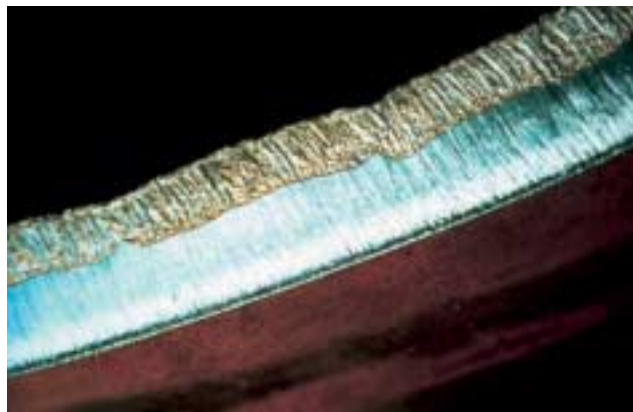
Schnitt durch eine Verschleißverbundplatte, bestehend aus einem 8 mm dicken Baustahlblech und einer 5 mm dicken Auftragschweißung aus Chromkarbiden
